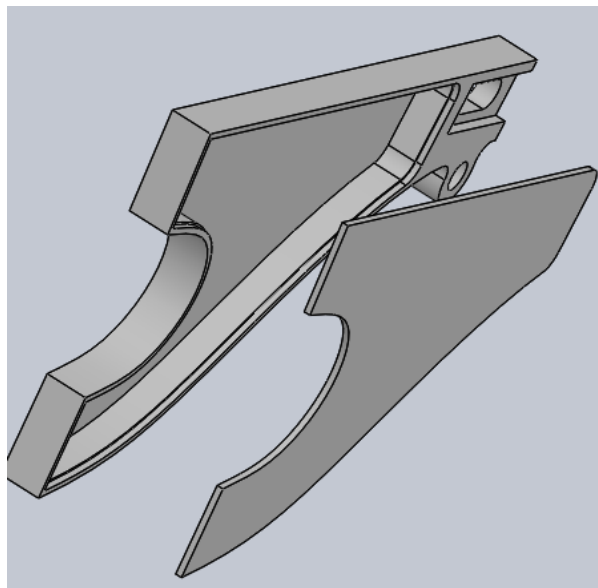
Vista explosionada del subensamblaje brazo derecho. [2]
